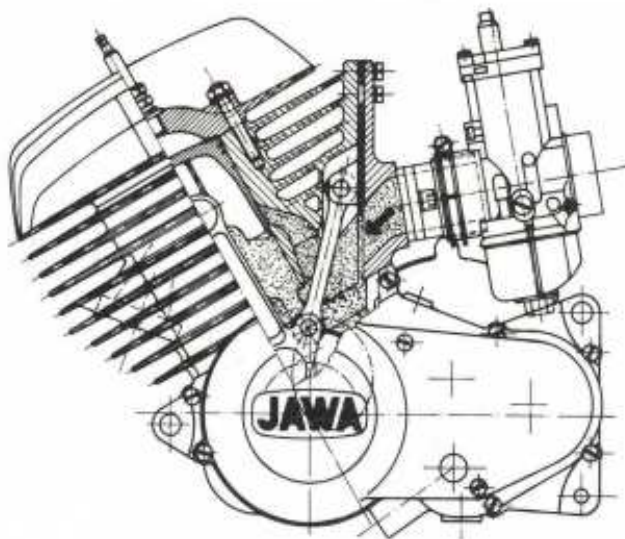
Rozvod sání rotačním šoupátkem [17]
